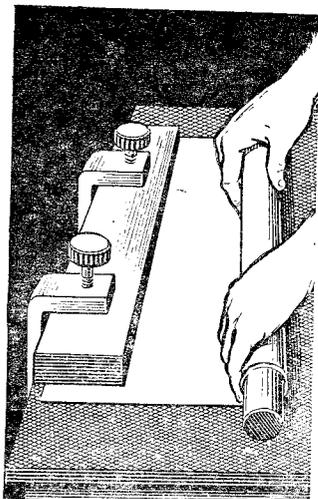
Изготовление корпуса модели ракеты из листового материала
